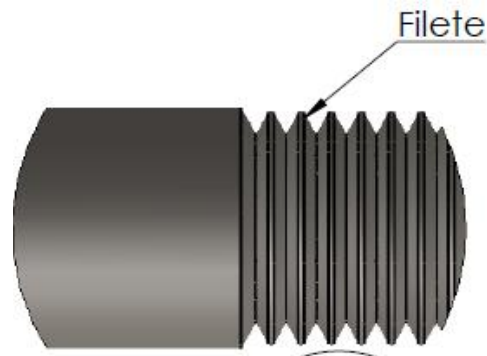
Filetes gerados em uma superfície cilíndrica.
